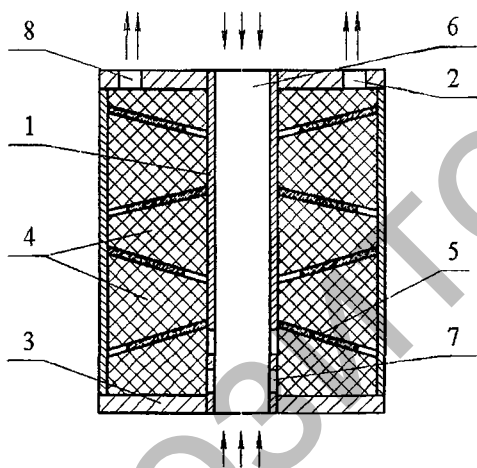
Схема ФЭ фильтра многостадийной очистки (пат. 1251 РБ): 1 – трубчатый каркас; 2 – верхняя крышка; 3 – нижняя крышка; 4 – фильтрующие диски из ДВПЯМ, 5 – прокладки; 6 – центровое отверстие; 7, 8 – отверстия
